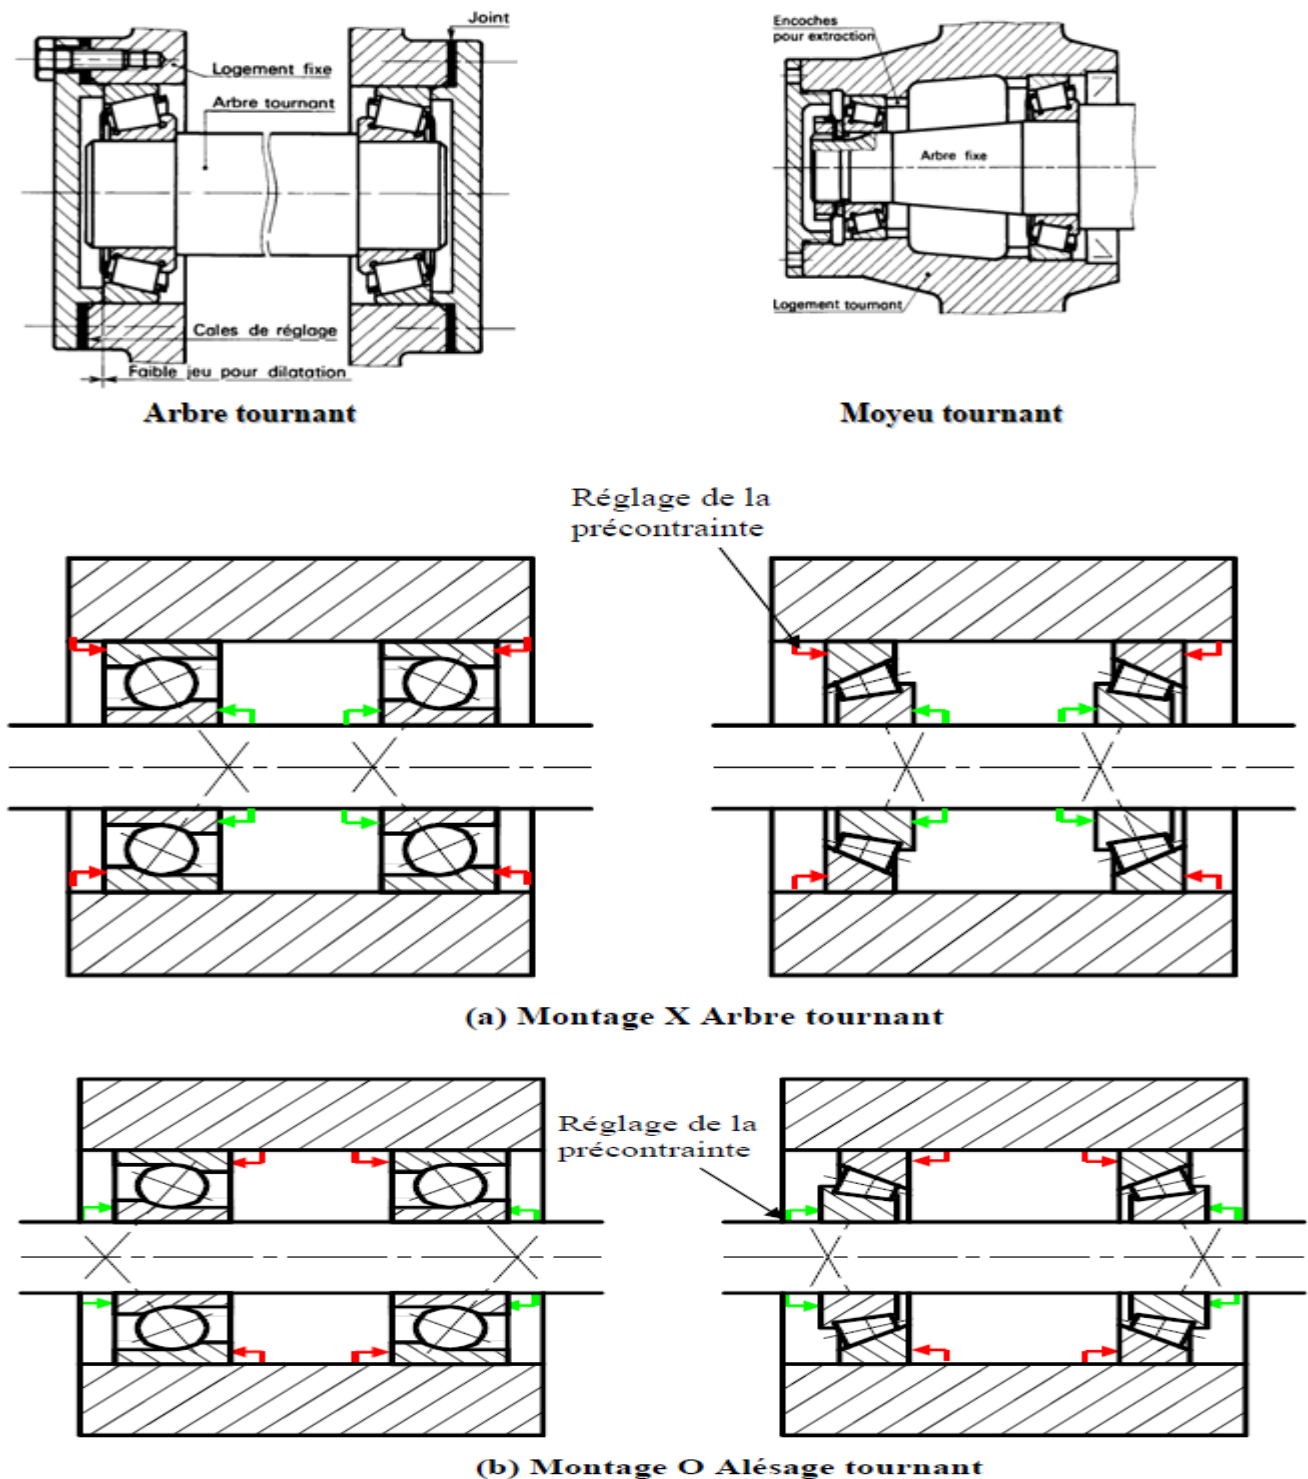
Montage des roulements à rouleaux ou à contact oblique
